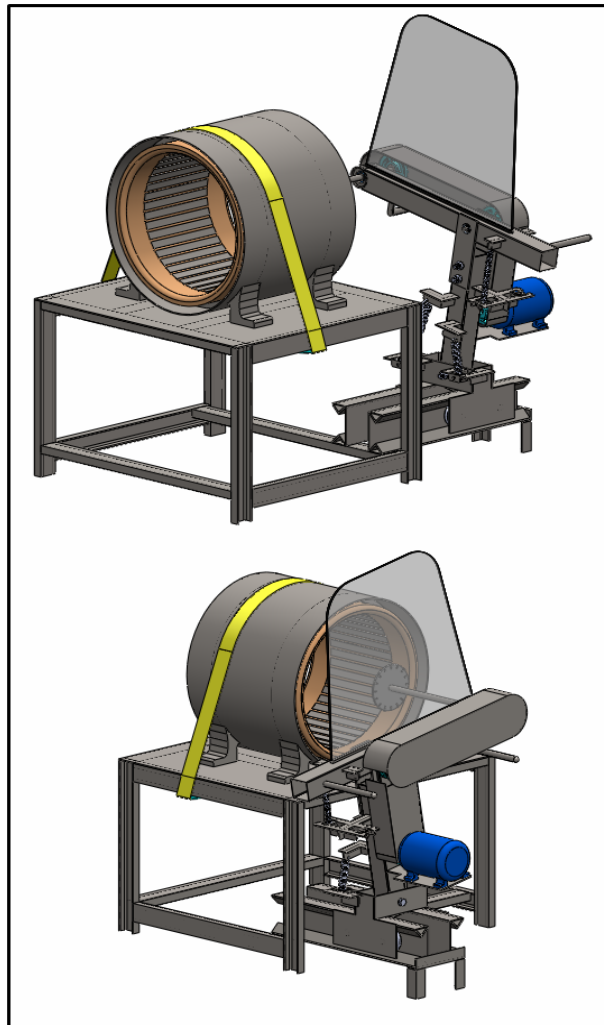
Vistas de la máquina horizontal seleccionada para su diseño [Fuente: propio].
